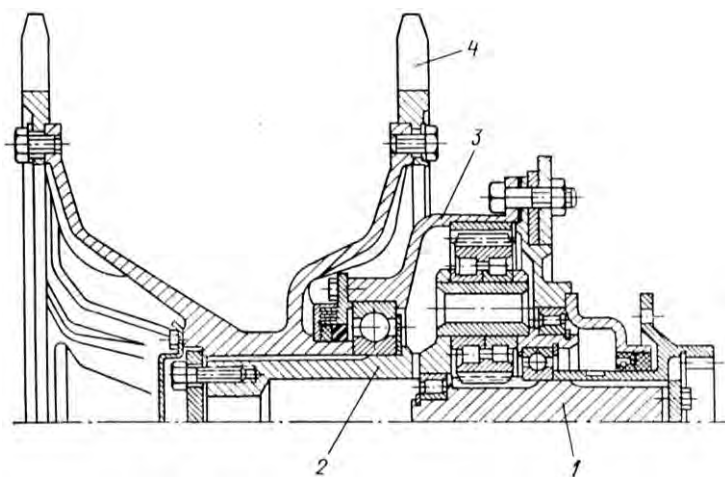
Конструкция однорядной планетарной бортовой передачи
